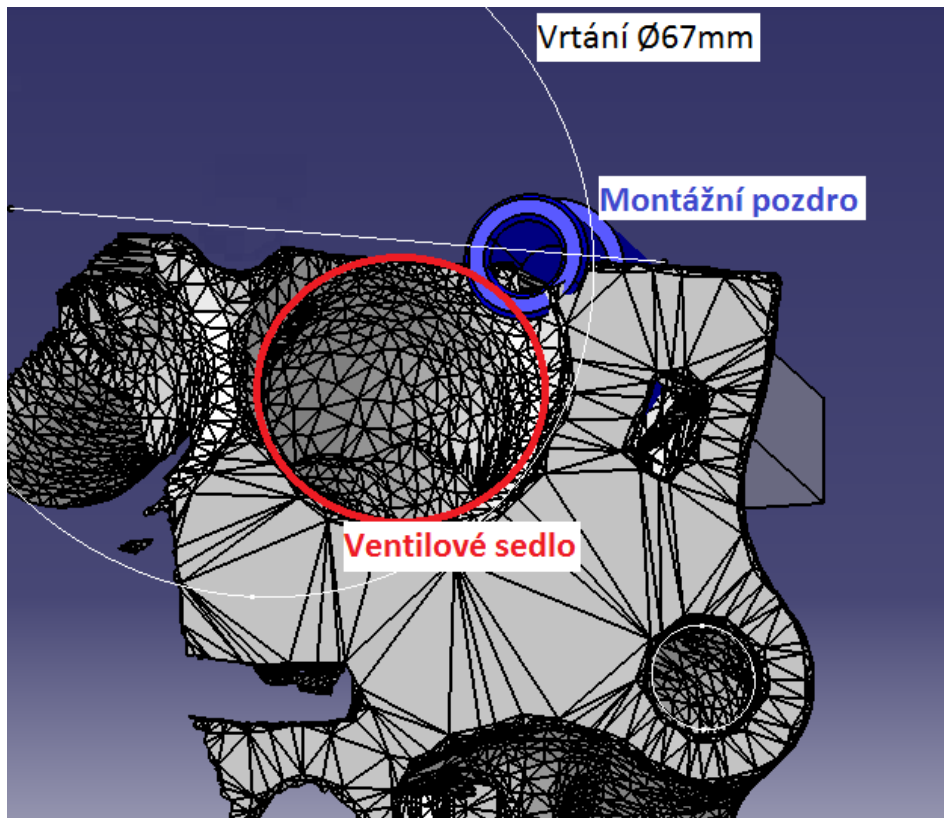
Scan řezu hlavou motoru- čtvrtý válec
